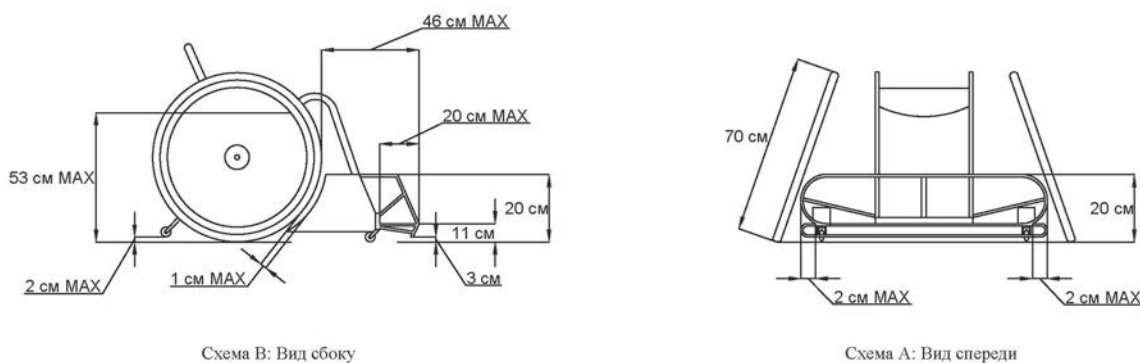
Схема и размеры кресла-коляски для регби на колясках
